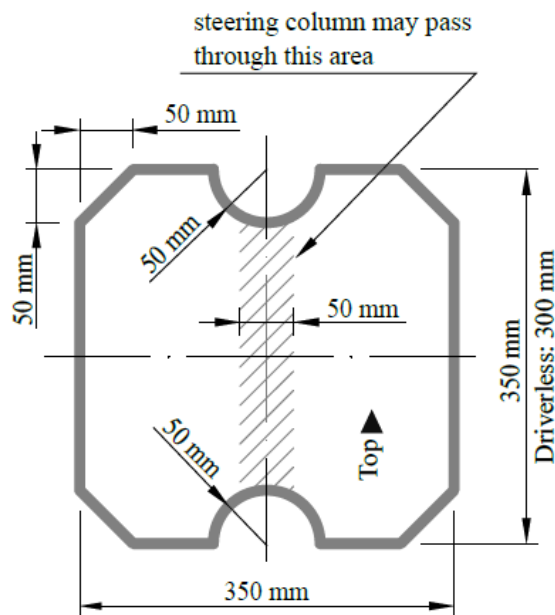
Plantilla utilizada para comprobar el espacio en las piernas del piloto [9]
